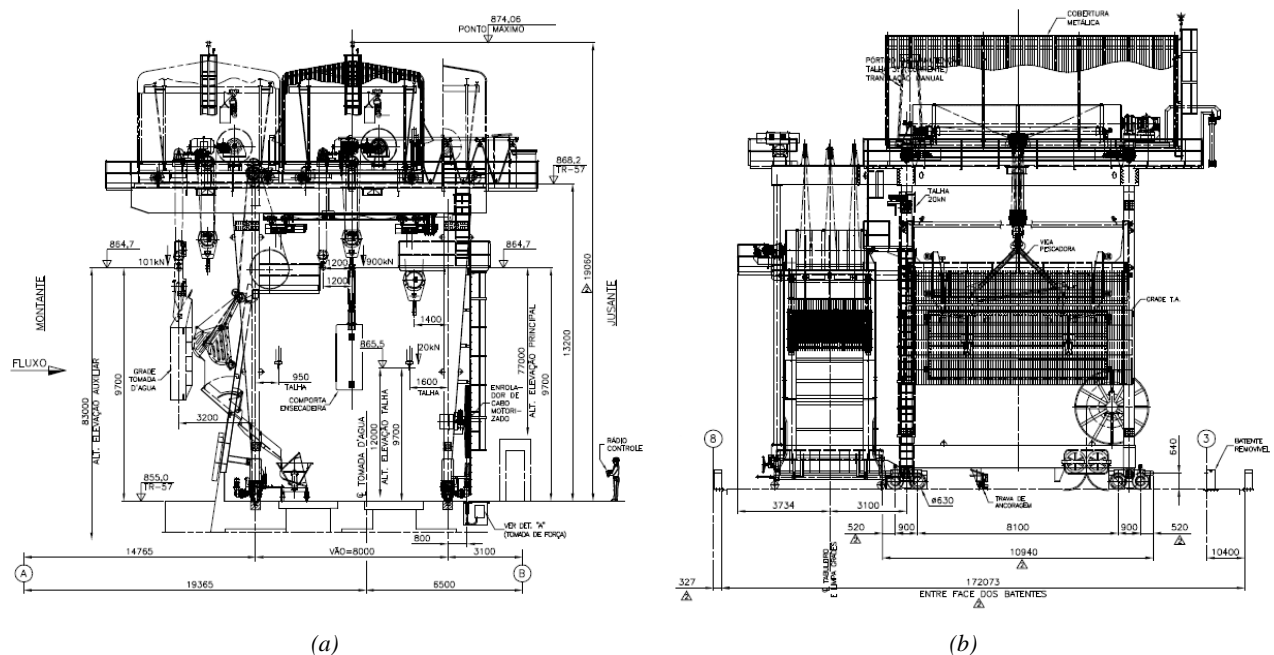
Pórtico grúa – (a) Vista frontal; (b) Vista lateral (Intertechne, 2014)
